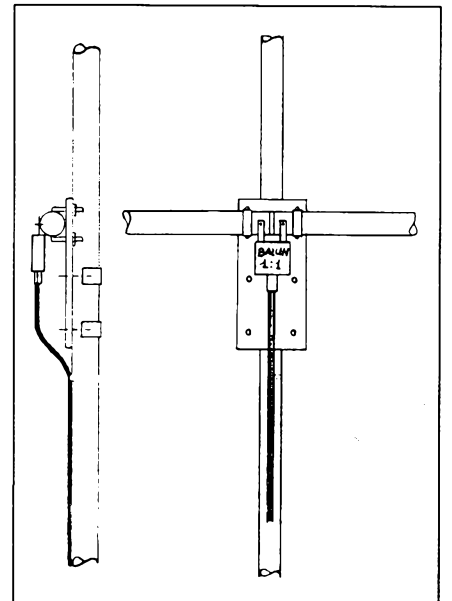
Rechts het vooraanzicht voor de bevestiging van de balun met roestvrijstalen strippen en M4 boutjes op de mast, links het zijaanzicht van deze constructie.
